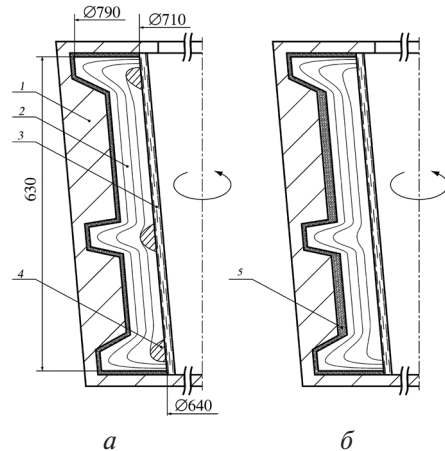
Схема нанесения теплоизолирующего покрытия для устранения бассейнов металла: 1 – изложница; 2 – отливка; 3 – шлаковая ванна; 4 – бассейны металла; 5 – теплопокрытие
